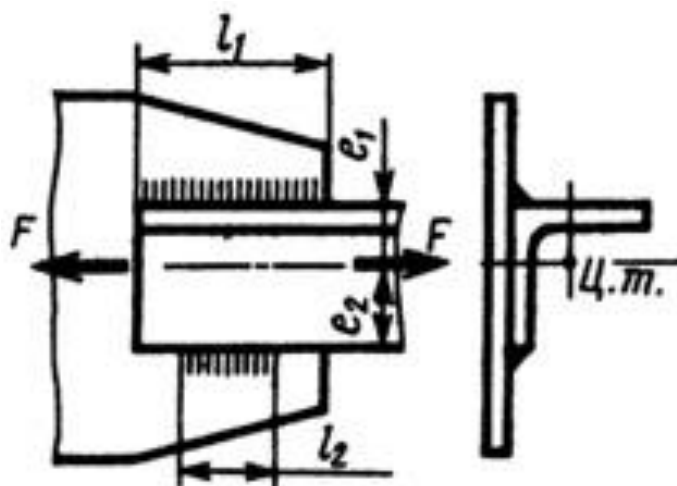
Сварное соединение с несимметричной деталью
